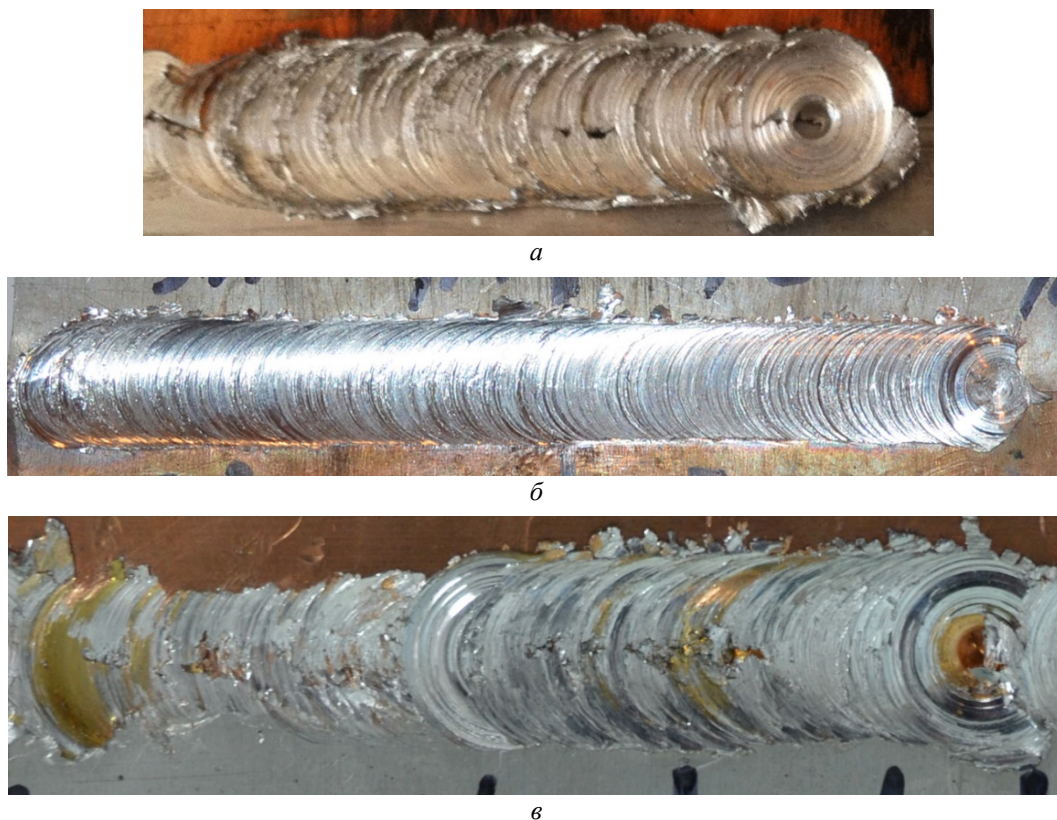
Морфология сварного шва при скорости сварки 25 мм/мин и угле наклона инструмента 3° от скорости вращения СИ об/мин:
